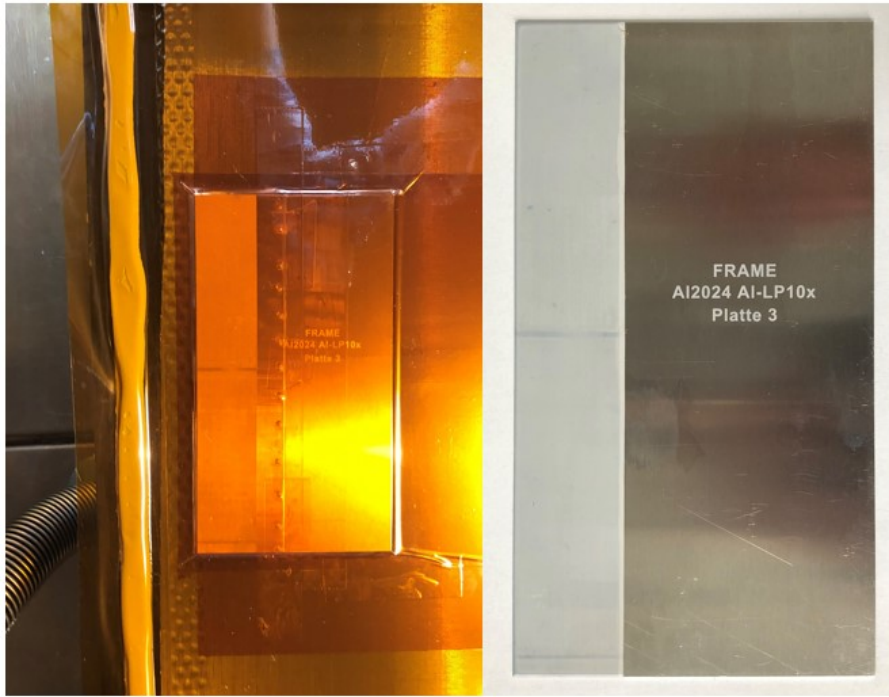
Aluminiumblech im Vakuum (links) sowie das beschichtete Aluminiumblech (rechts)
